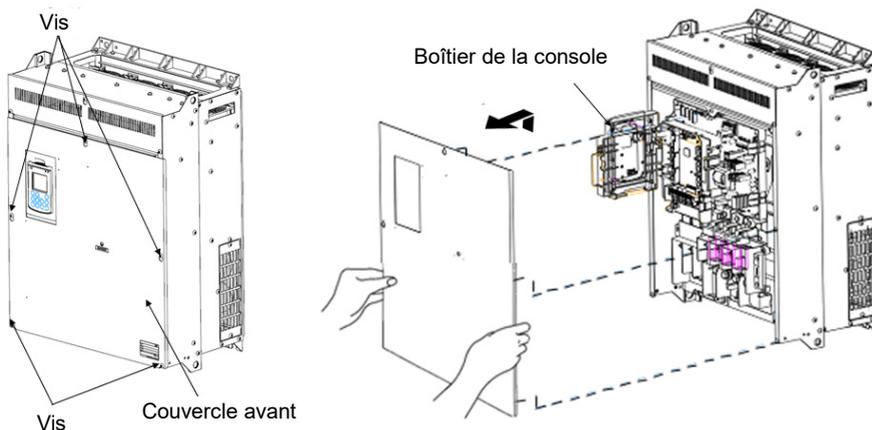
Retrait du couvercle avant et de la plaque de câblage (FRN110AQ1S-4□)
